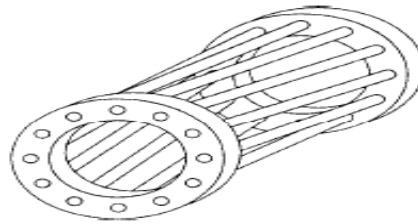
Rotor à cage d'écureuil de la machine asynchrone.
